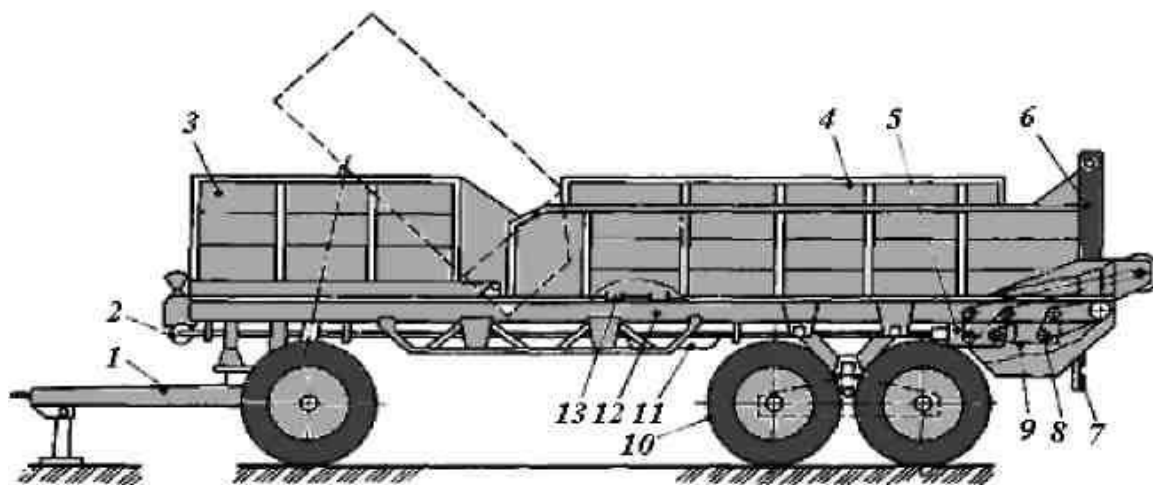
Прицепной тракторный разбрасыватель ПРТ-16: 1 – прицепное устройство; 2 – карданная передача; 3 и 4 – секции кузова; 5 и 9 – редукторы; 6 – разбрасывающее устройство; 7 – электрооборудование; 8 – сменная звездочка; 10 – балансирующая подвеска; 11 – тормозная система; 12 – рама; 13 – транспортер-дозатор
